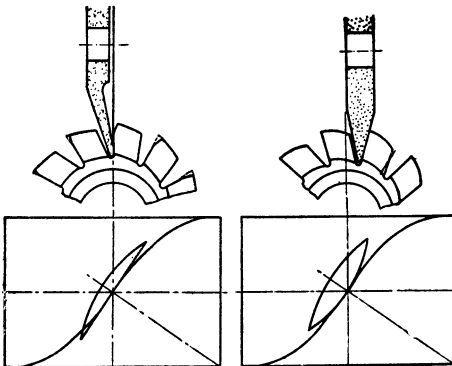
Schleifen spiralgenuteter hinterdrehter Fräser.
